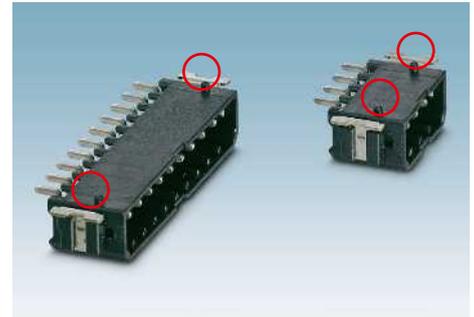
Steckverbinder mit Positionierzapfen (Mounting Bosses)
